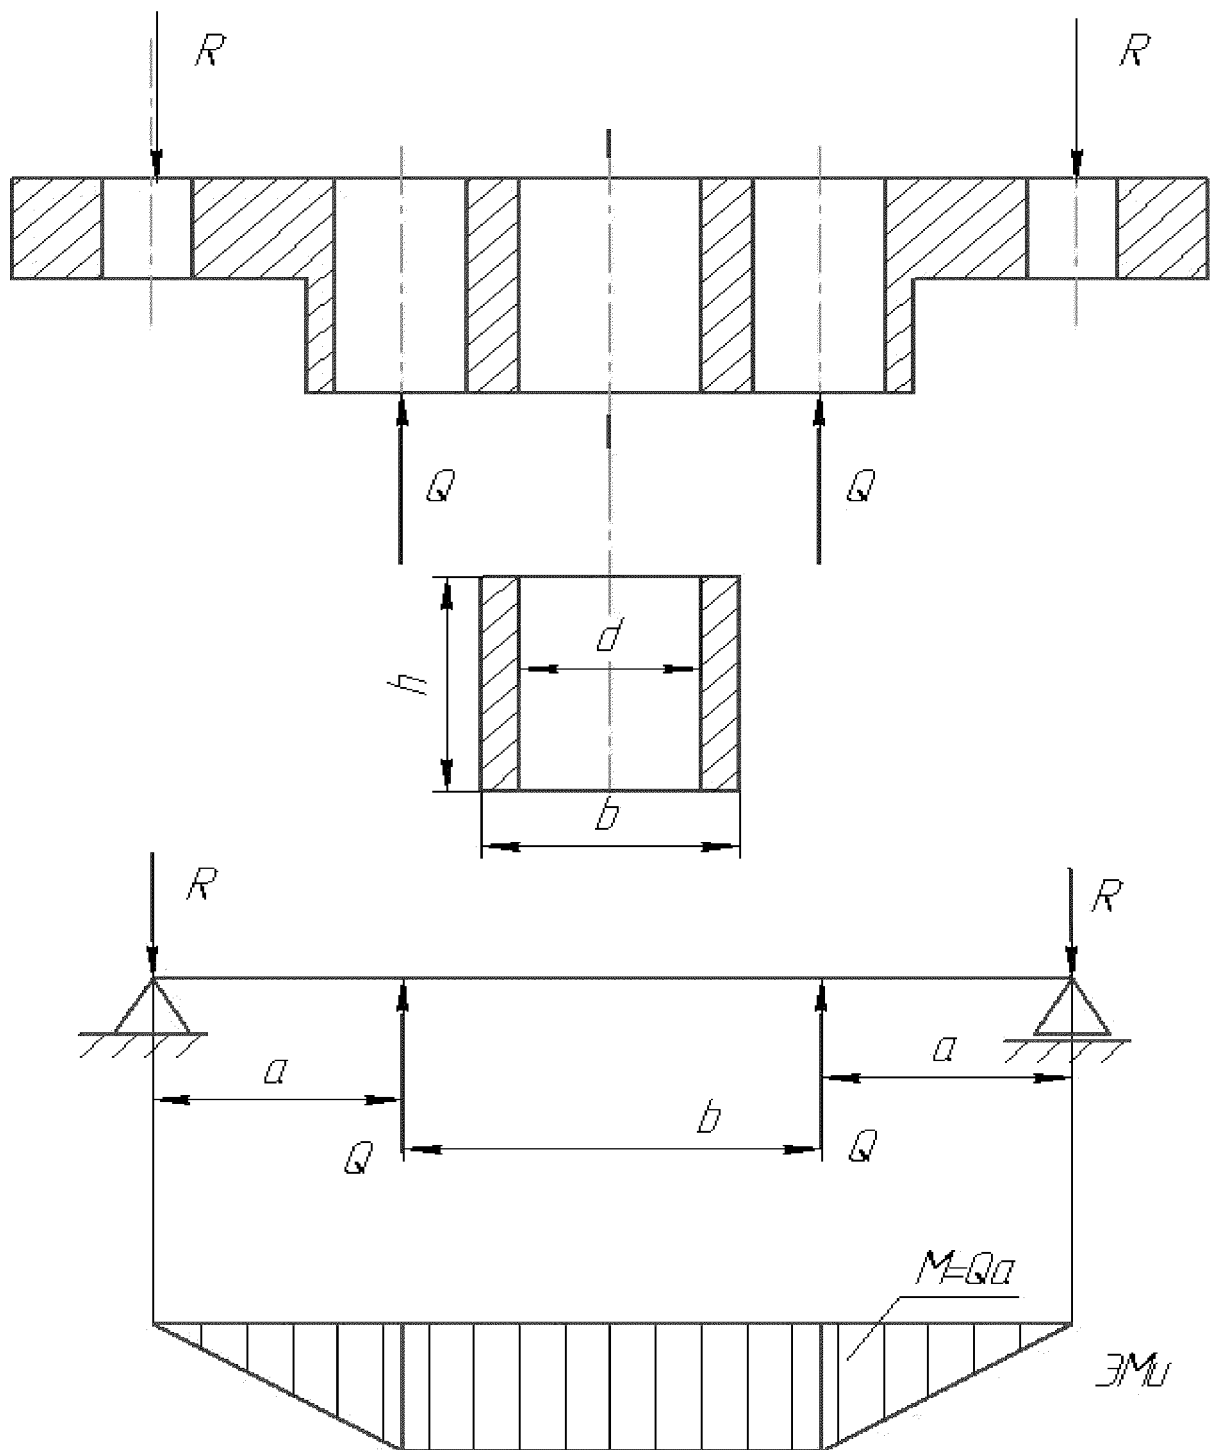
Расчётная схема корпуса блока цилиндров
